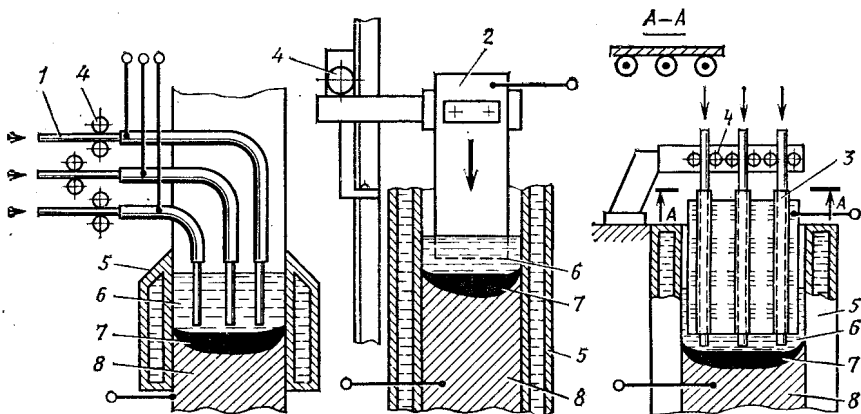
Способы электрошлаковой сварки:
